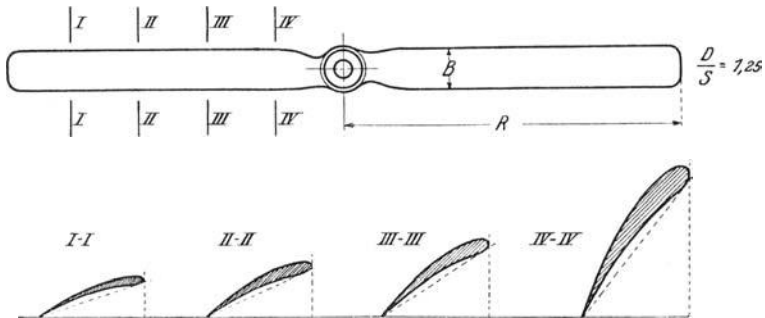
u. 74. Ansicht und Querschnitte einer Luftschraube.
